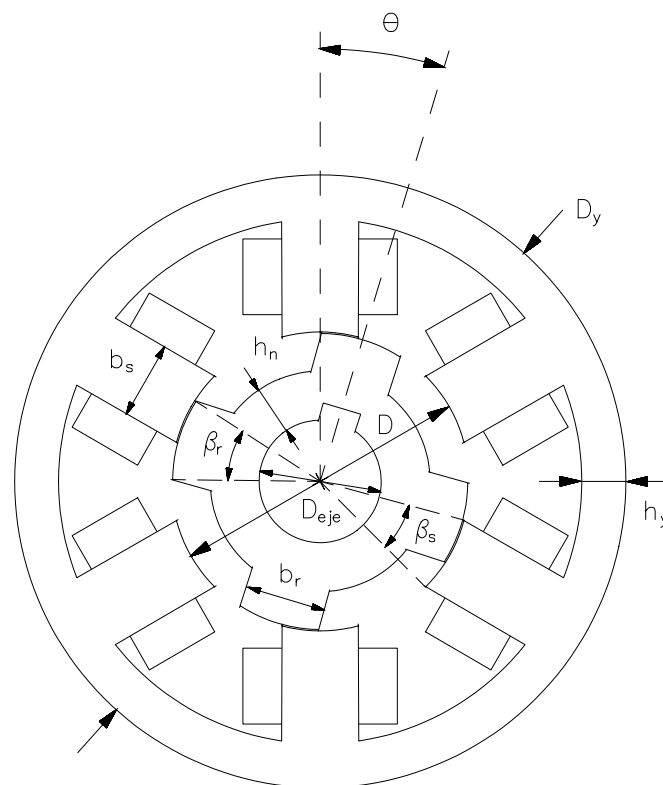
Dimensiones geométricas principales de la estructura electromagnética.
